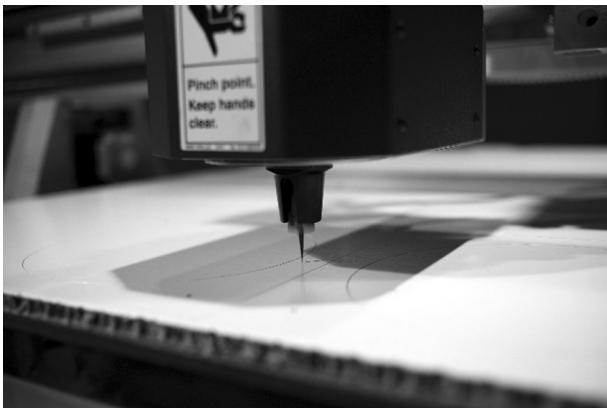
O material da instalação, sendo usinado por corte a lâmina.
